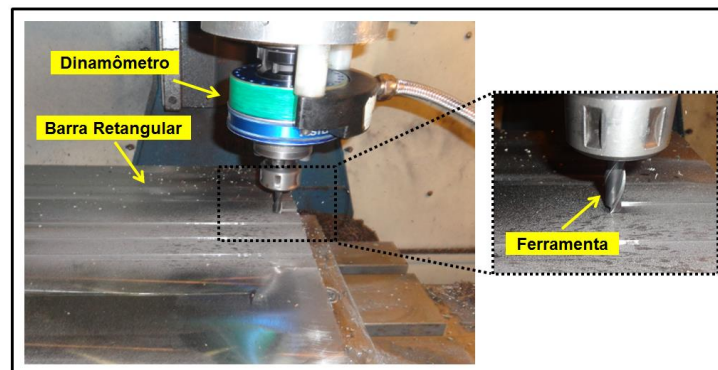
Montagem do dinamômetro rotativo no interior do centro de usinagem
